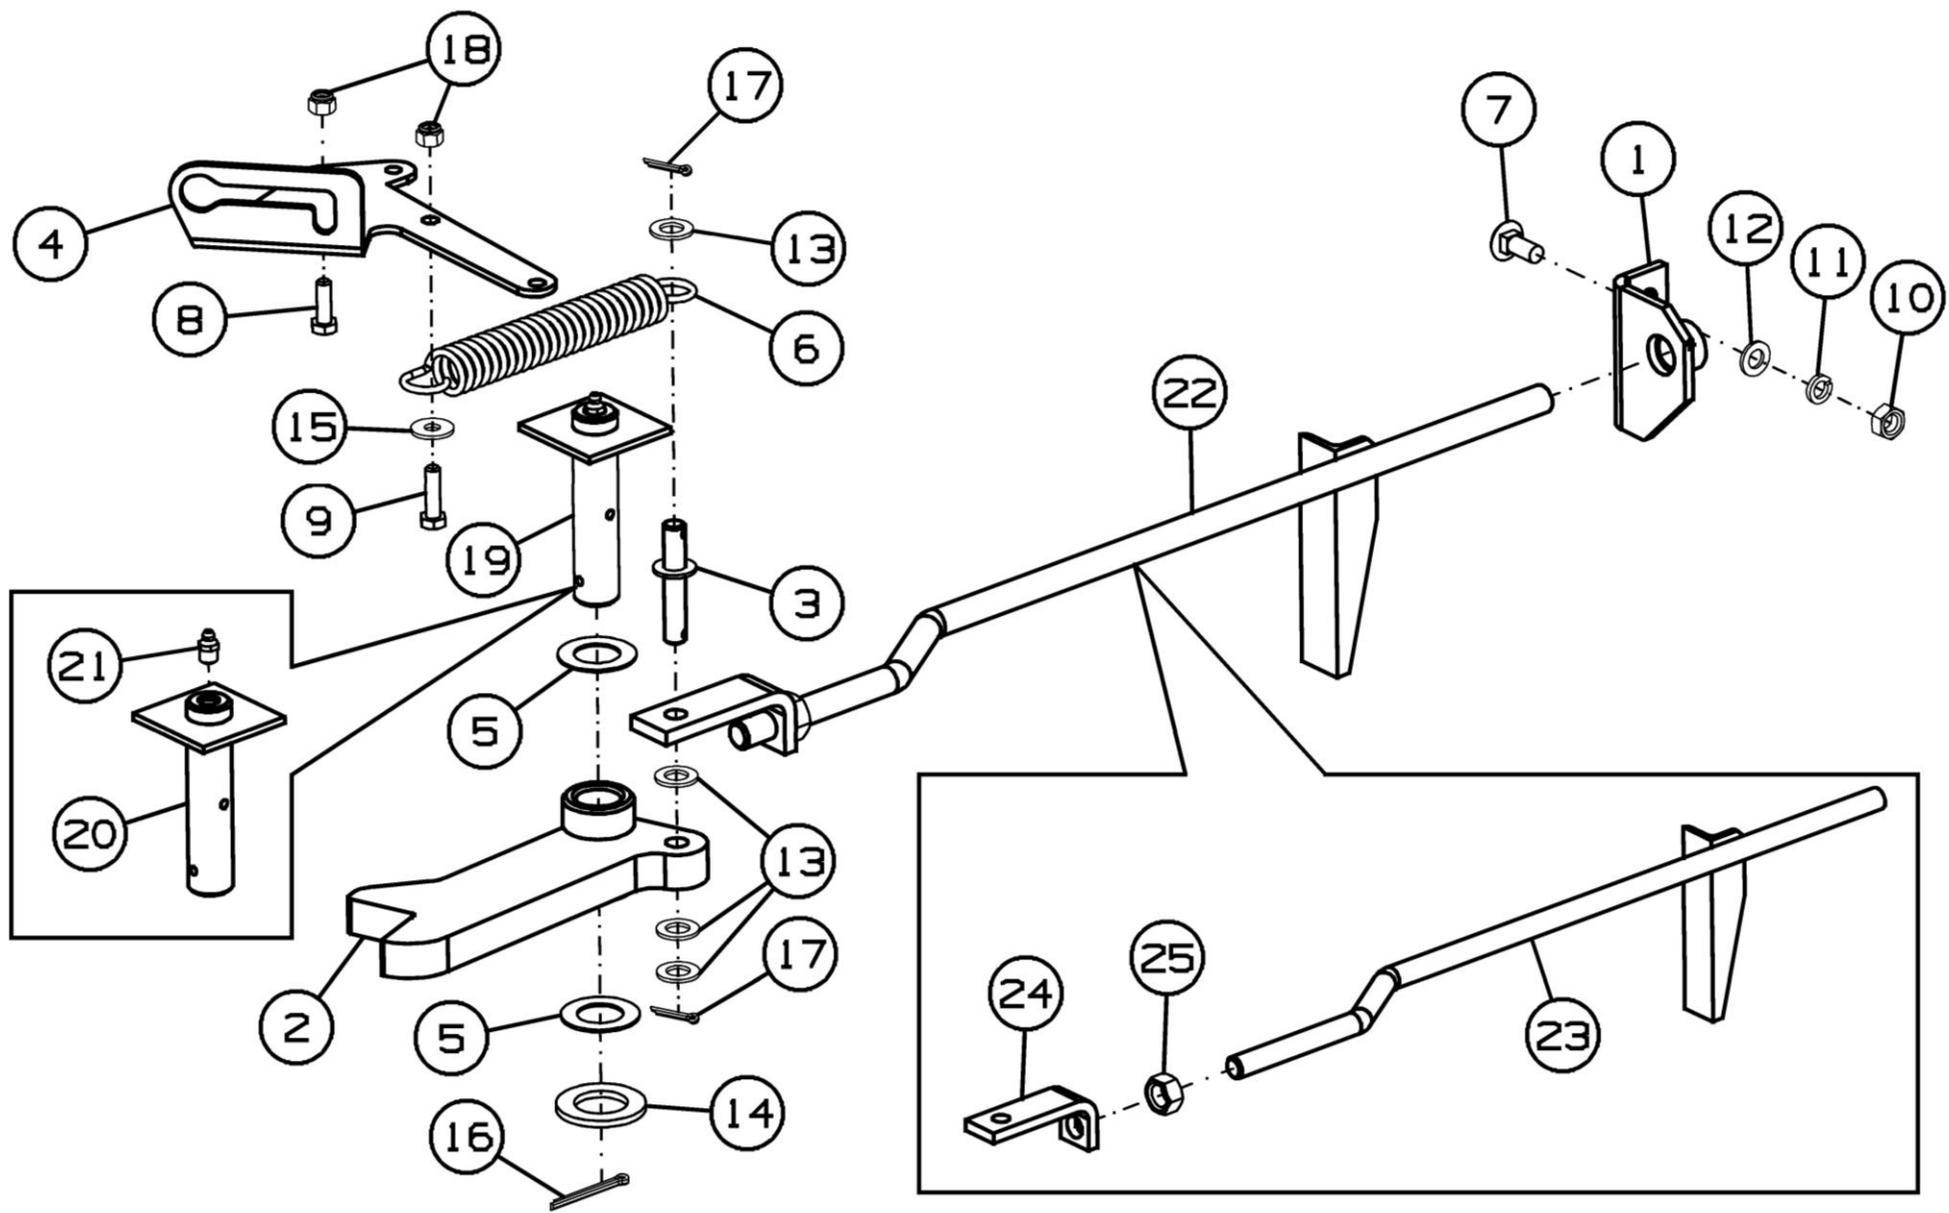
Установка предохранителя ППТ-041.01.300
